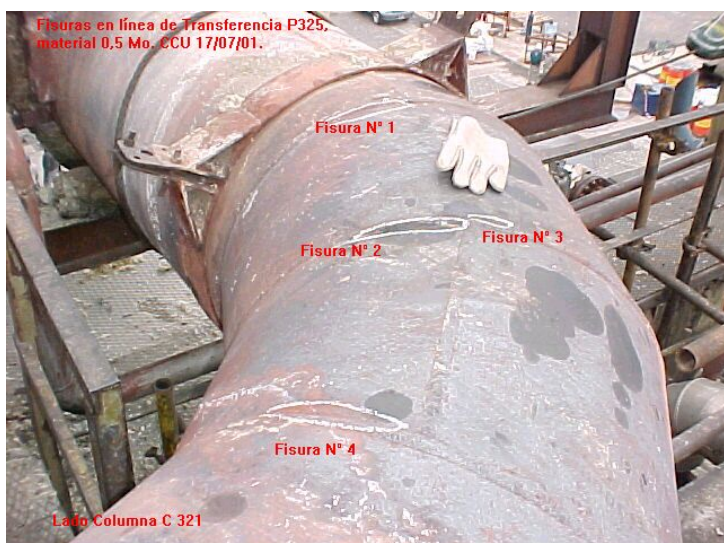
Fisuras en cañería de tope del reactor
